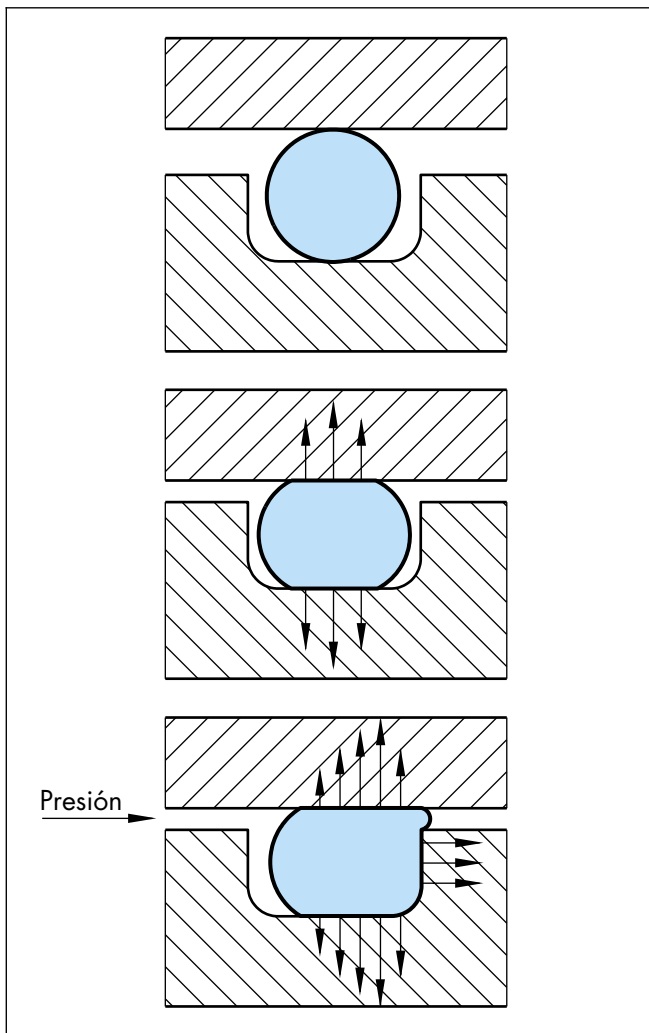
Fuerzas de estanquidad de una junta tórica con y sin presión del sistema
